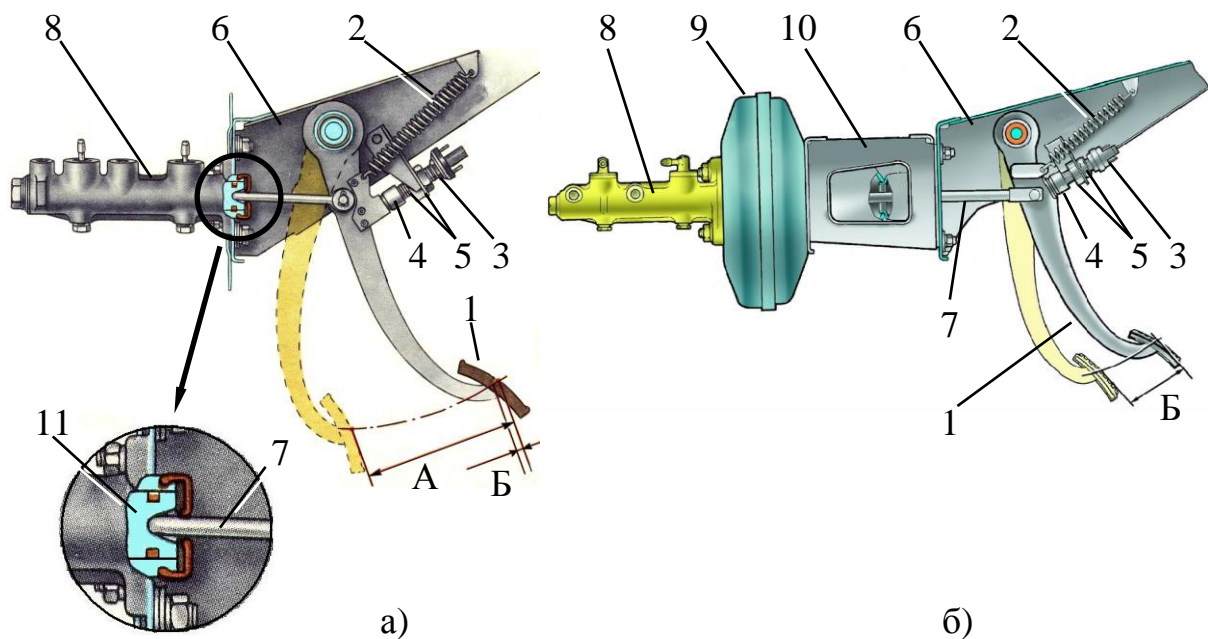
Конструкция органа управления с гидравлическим тормозным приводом: а – без усилителя, б – с усилителем; 1 – педаль тормоза; 2 – оттяжная пружина педали; 3 – выключатель стоп-сигнала; 4 – буфер выключателя стоп-сигнала; 5 – гайки; 6 – кронштейн крепления педали; 7 – толкатель; 8 – главный тормозной цилиндр; 9 – усилитель тормозного привода; 10 – кронштейн вакуумного усилителя; 11 – поршень главного тормозного цилиндра; А – полный ход педали; Б – свободный ход педали
